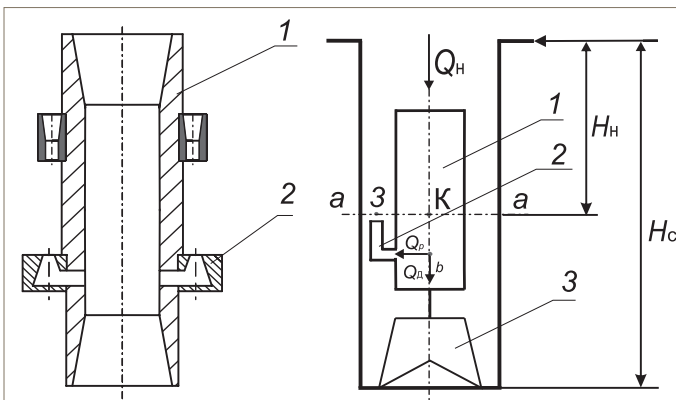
Конструкція (а) та гідравлічна схема (б) ежекційної системи для буріння свердловин: 1 – корпус пристрою; 2 – робоча насадка струминного насоса; 3 – долото
